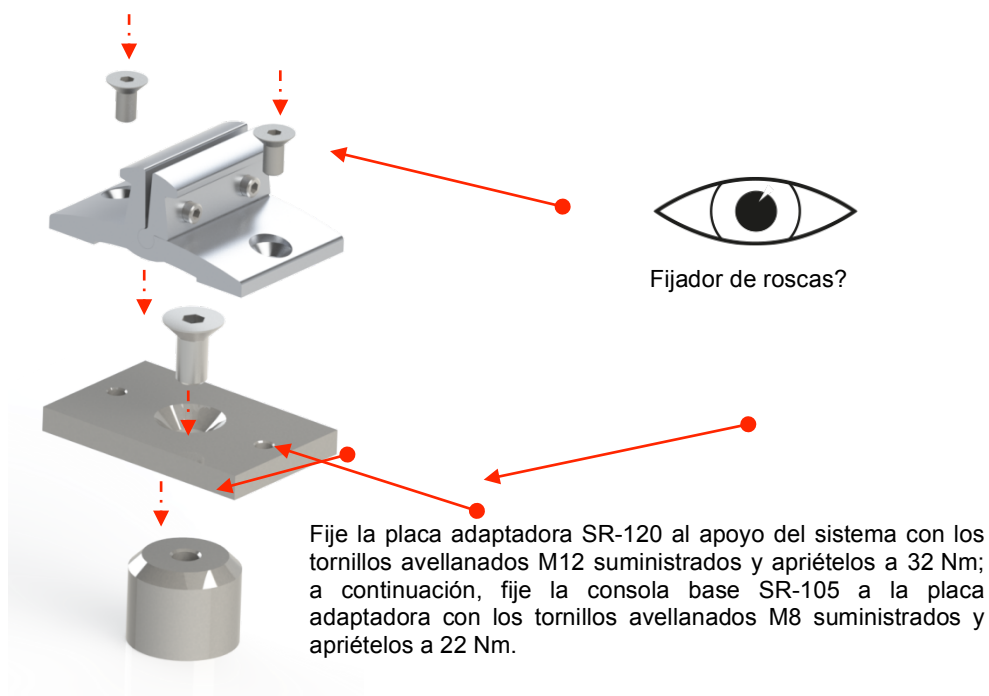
Montaje de la consola básica SR-105 en la placa adaptadora SR-120
